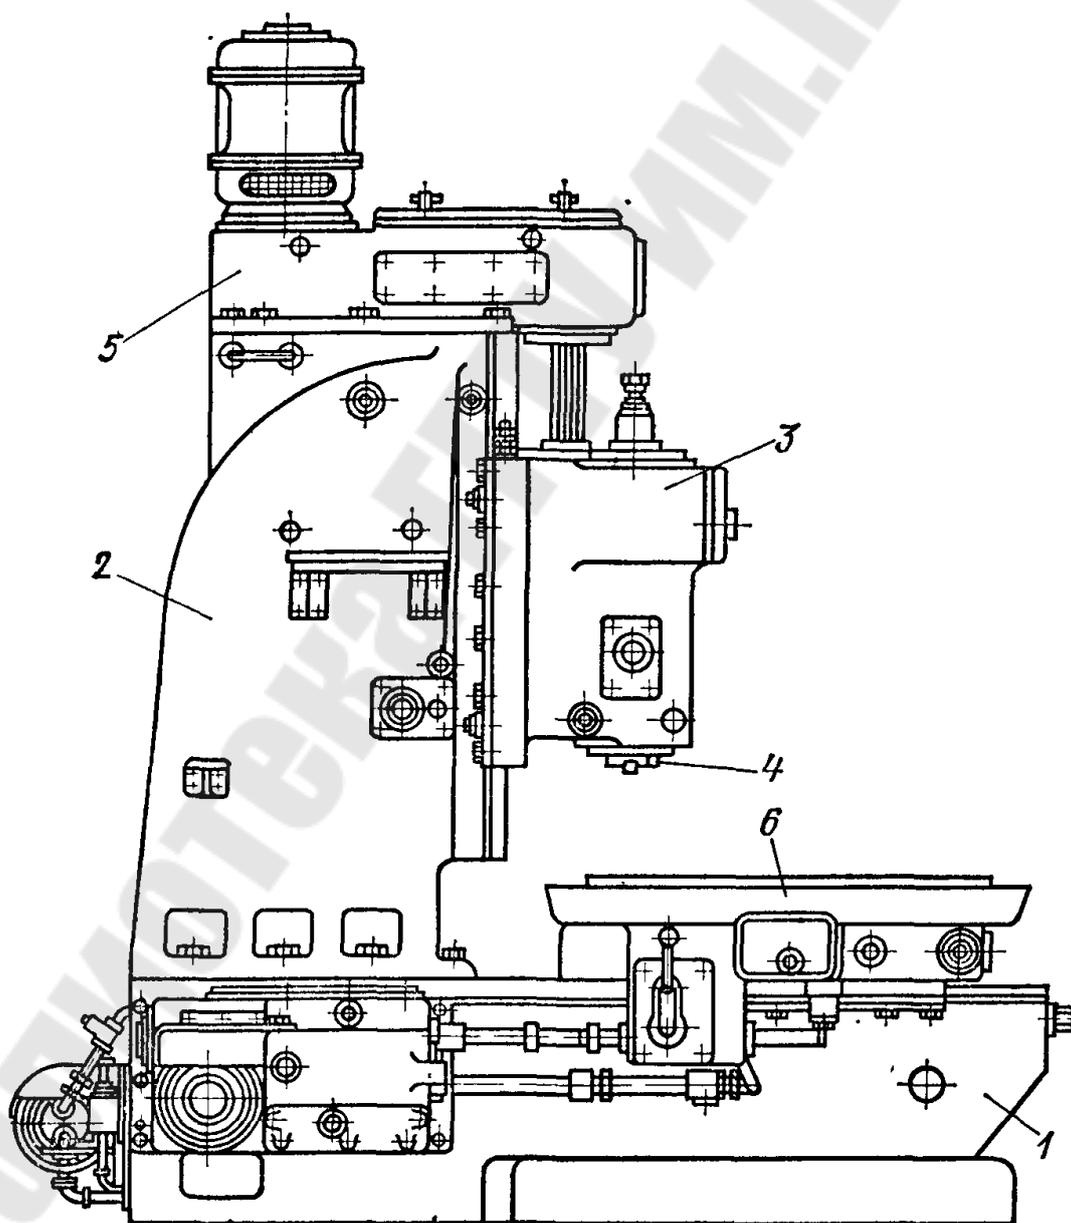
Общий вид карусельно-фрезерного станка
